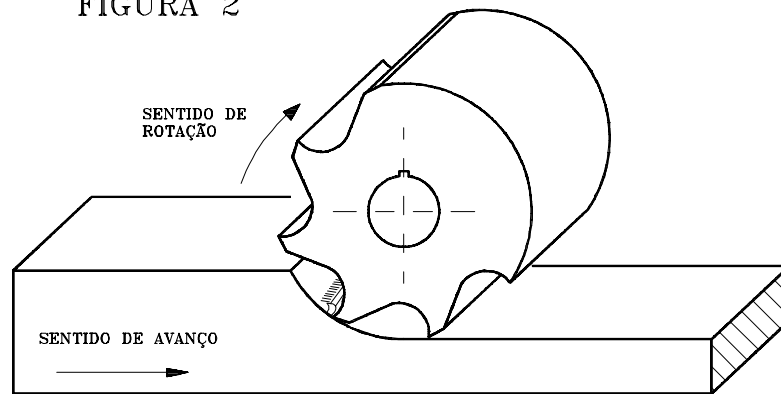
Fresamento tangencial com sentido de movimento discordante
